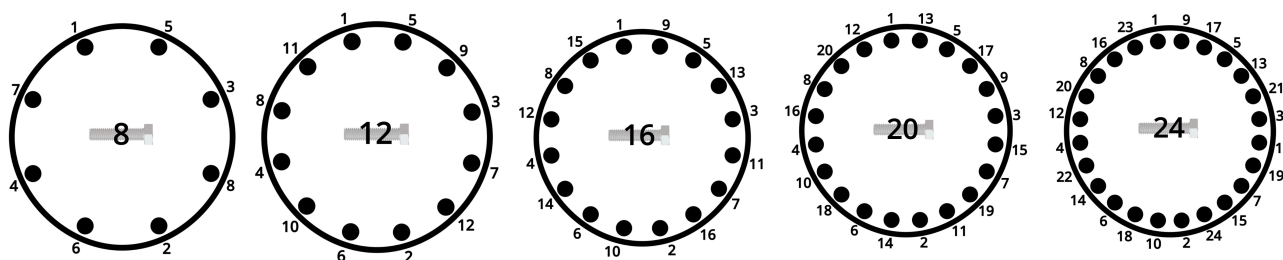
Sequenza del raccordo filettato della flangia del tubo
